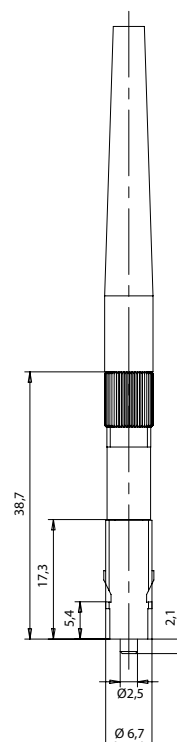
Abmessungen SC-Klemmsteckverbinderkontakt
